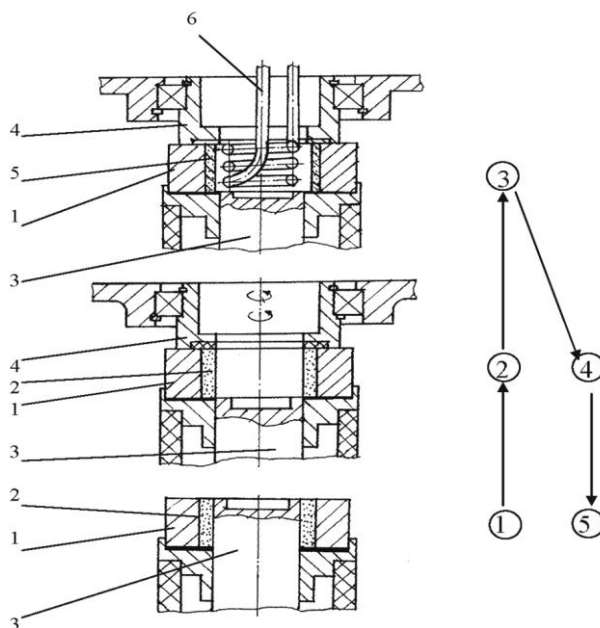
Шестерня 2-й передачи вторичного вала коробки передач ЯМЗ №236-1701127 автомобиля КаМАЗ, нуждающаяся в восстановлении только внутренней поверхности:
